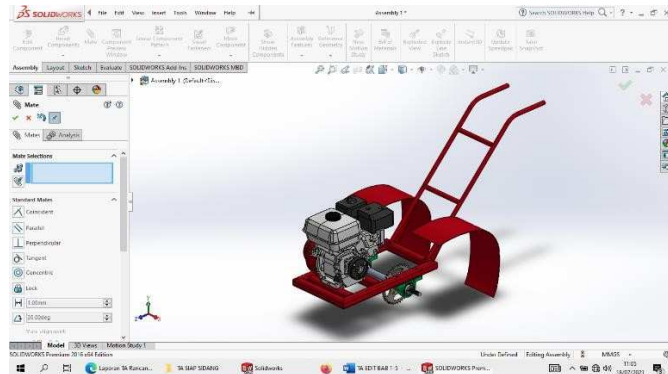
148 Hasil *Assembly* Mesin Penggerak dan *Clutch
